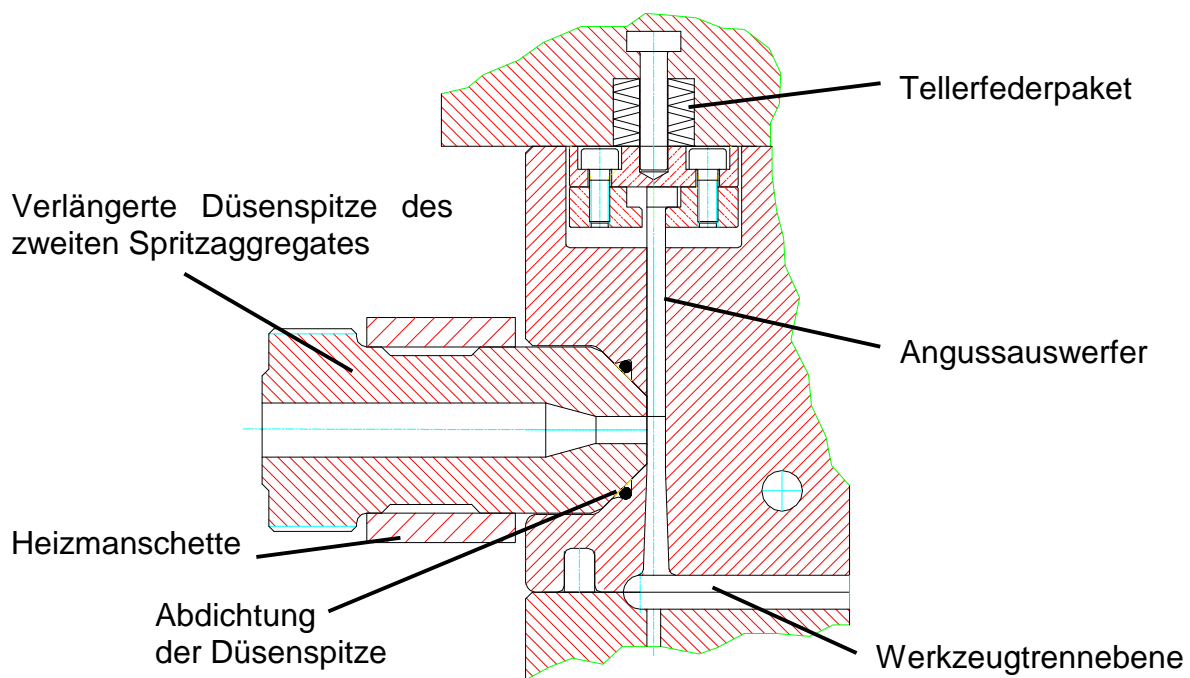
Schnittansicht des Entformungsmechanismus unterhalb des Angusskegels der zweiten Komponente
